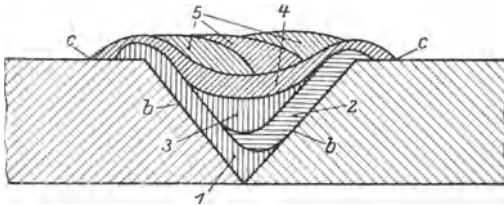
Anordnung der Schweißlagen bei Gußeisenkaltschweißungen.
